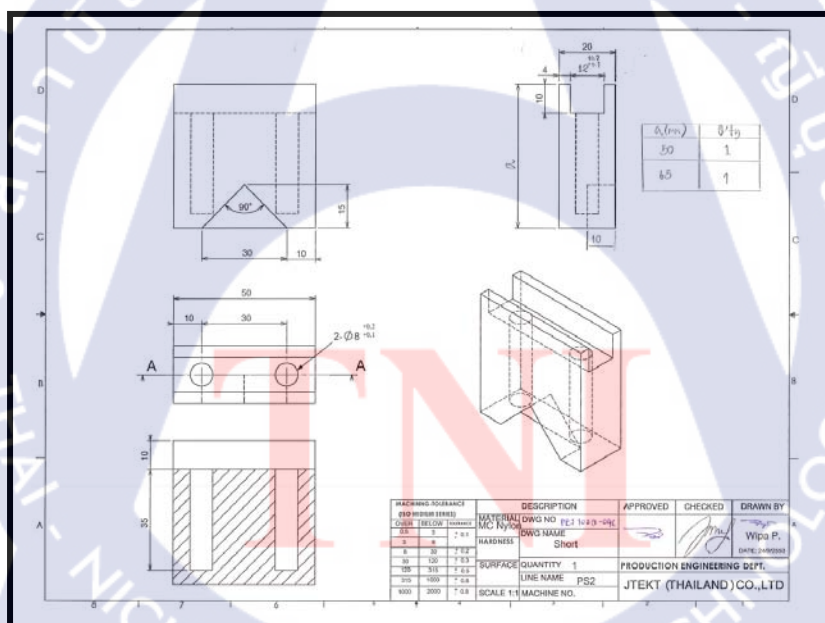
แสดงแบบฐานล่าง Jig support กับ โต๊ะ Deburring
